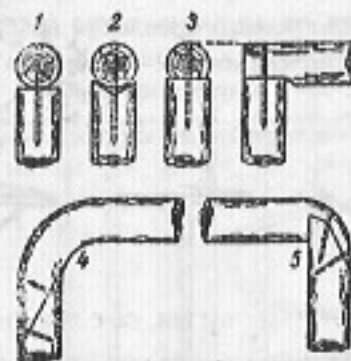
Угловые соединения деталей внакладку палки на торец:
